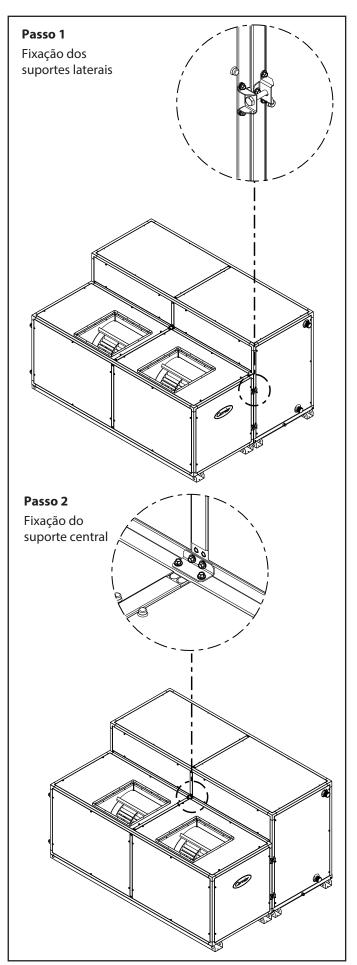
Detalhe de fixação dos módulos para montagem horizontal
